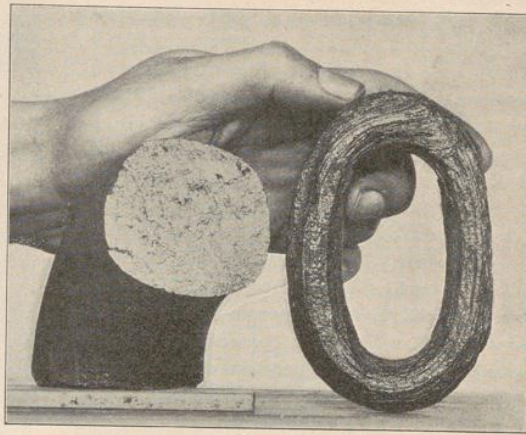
Eisen. Links Bruch eines Kettengliedes aus zu wenig sehnigem, also zu körnigem Schweißisen; rechts Kettenglied, welches seit vielen Jahren dem Seewasser ausgesetzt gewesen ist, sodaß die weichen Theile weggeätzt sind und man das sehnige Gefüge sowie oben die Schweißstelle deutlich erkennen kann.
